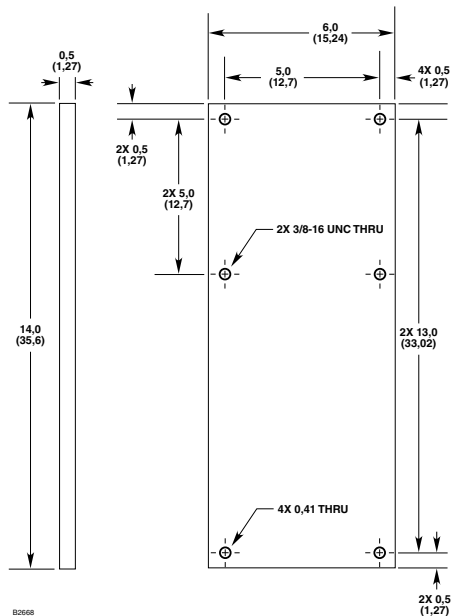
Размеры монтажной пластины 012718-003 для установки на плоской поверхности в дюймах (см)
